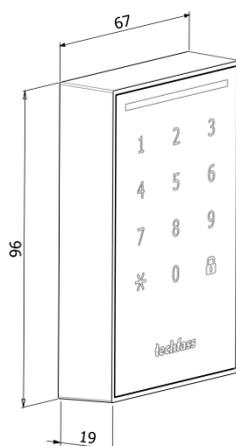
Dimensioni del lettore WRE121K e WRE 121A
